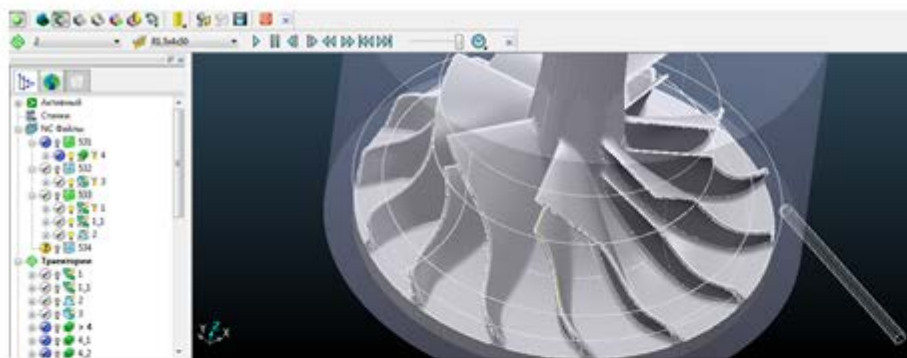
Траєкторії чорнової та чистової обробки заготовки.
